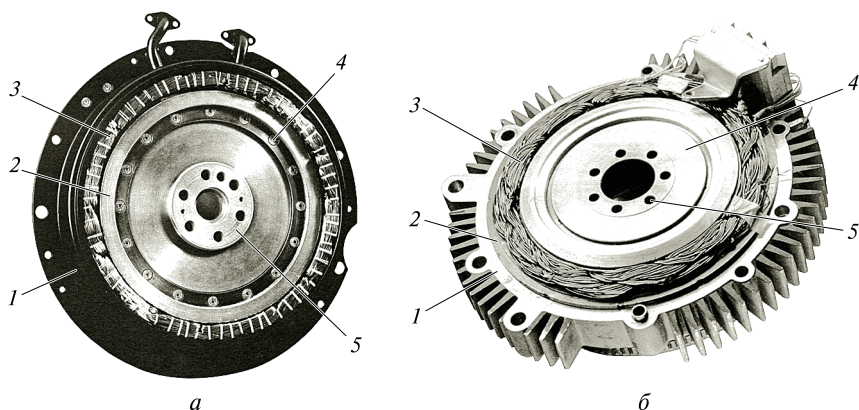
Конструктивные схемы стартера-генератора с водяным (а) и воздушным (б) охлаждением корпуса:
